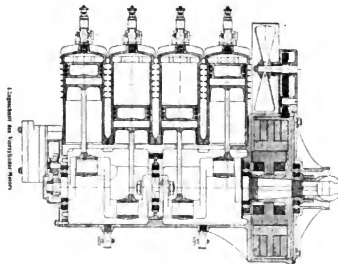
Dürckopp-Vierzylindermotor, Längsschnitt.
